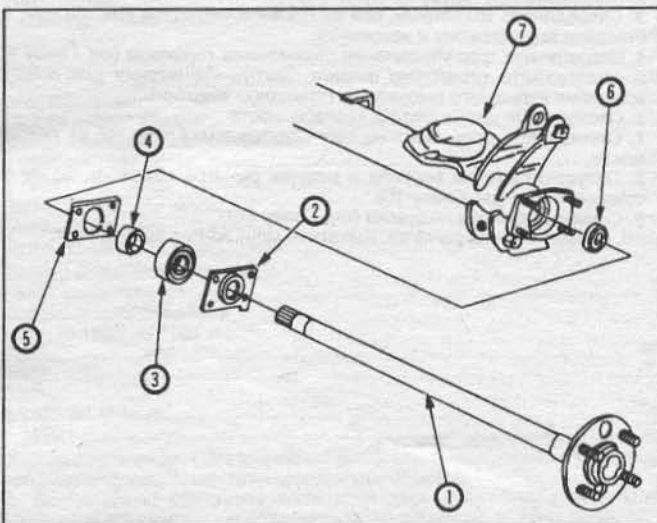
Детали заднего моста (1985 - 1987 годов): 1 - полуось; 2 - держатель полуоси; 3 - подшипник; 4 - держатель подшипника; 5 - проставка; 6 - сальник; 7 - мост.
